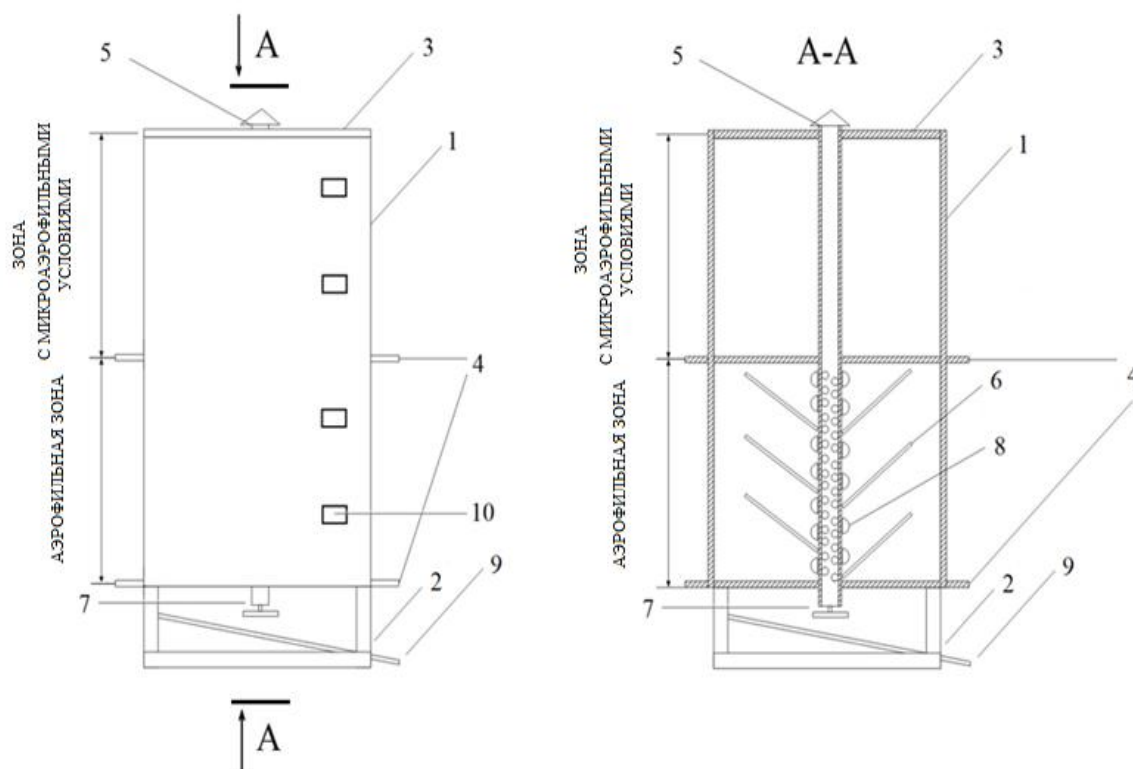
Конструкция биореактора: 1- корпус биореактора; 2 – опорная рама конструкции; 3 - загрузочный люк; 4 - отсечные шиберы; 5 - аэрационная труба; 6 - разгружающие элементы; 7 - электропривод; 8 – орошающее устройство; 9 – лоток для переработанного субстрата; 10 – технологические люки.
